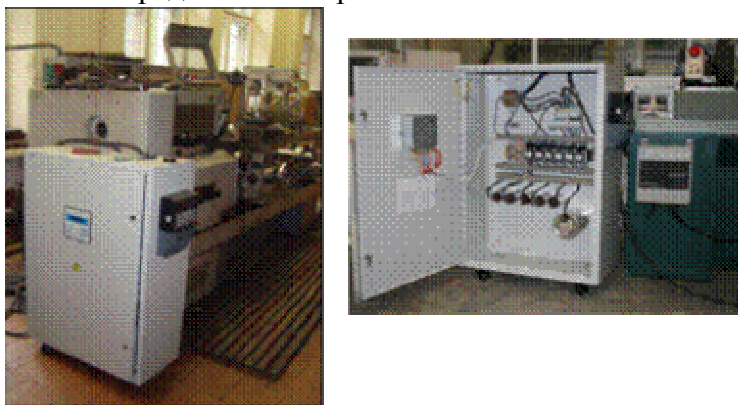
Общий вид установки АККРМ-1 для токарного станка 16К20
